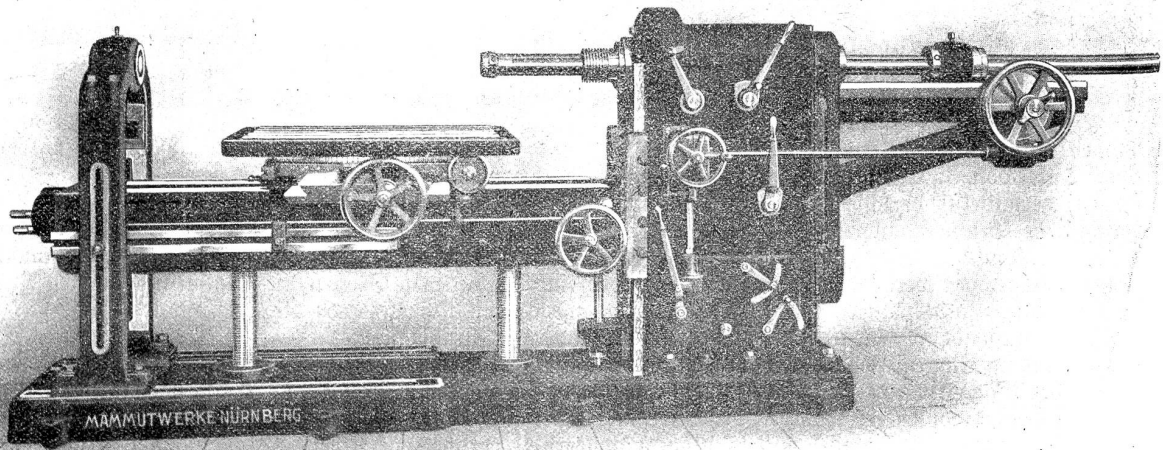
Horizontale Bohr- und Fräsmaschine mit Einscheibenantrieb Type S H F 2.
